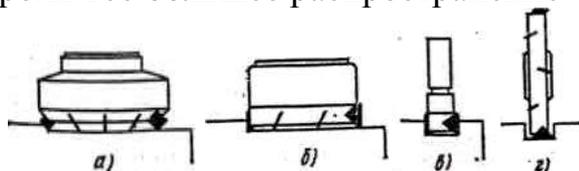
Набор фрез с неперетачиваемыми пластинками
